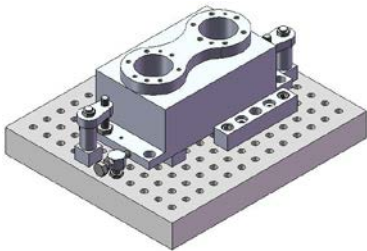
Компонування верстатного пристрою для обробки корпусної деталі
